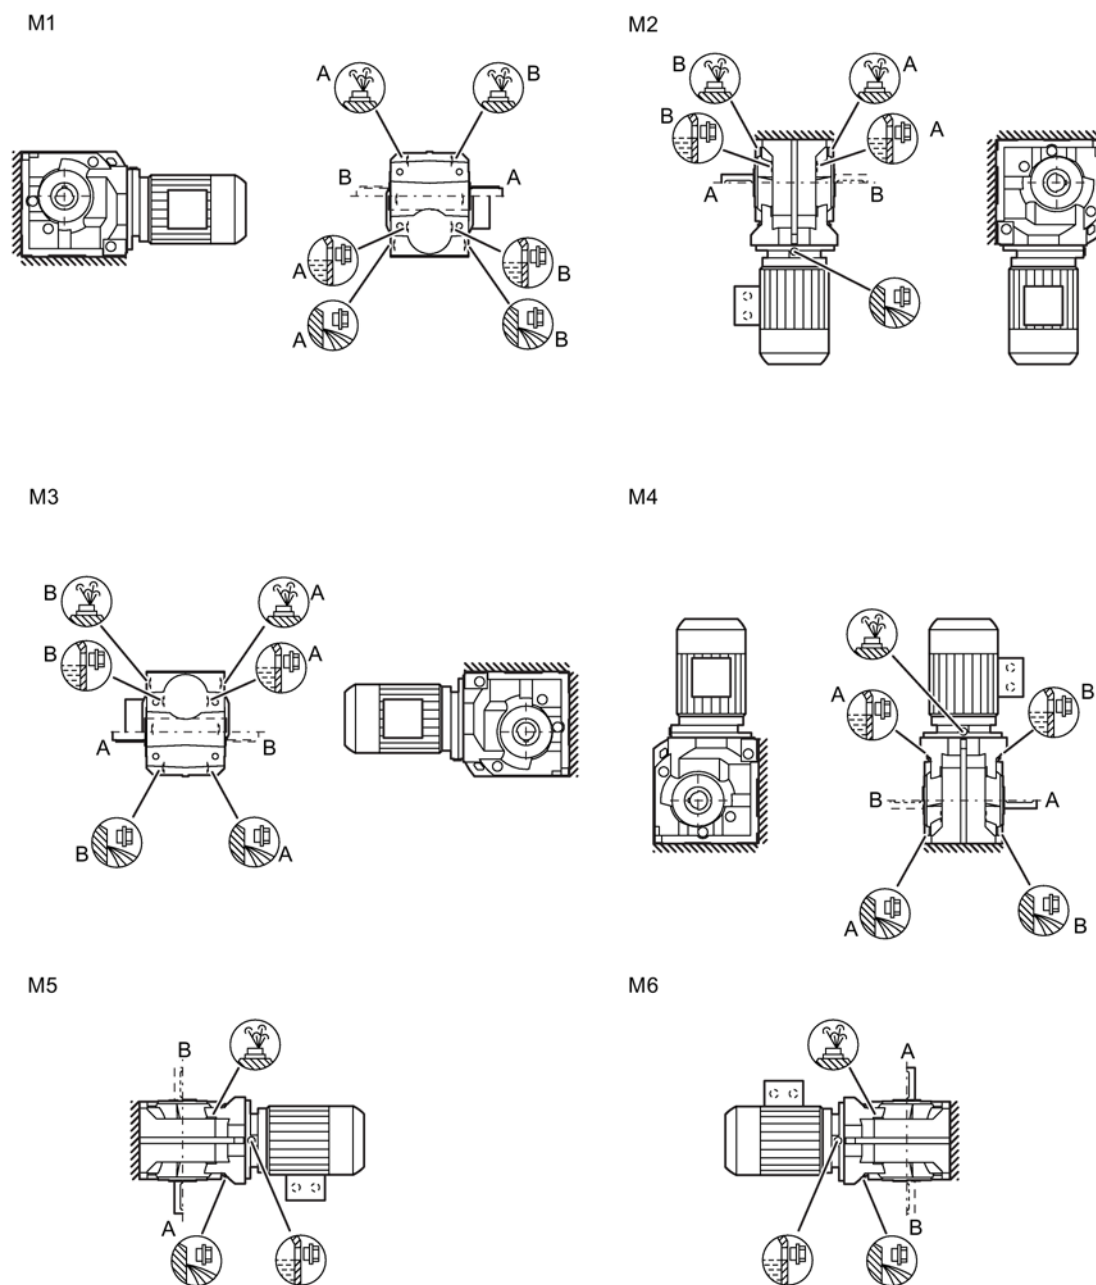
Монтажные положения для цилиндрического косозубого редуктора С. в исполнении на лапах, типоразмер 39- 89
